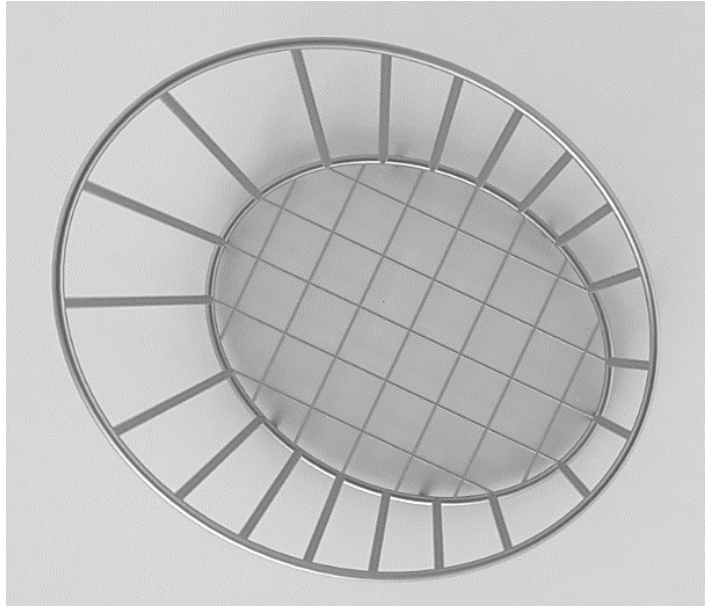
Vista superior estructura de aluminio (Fuente: Propia)
